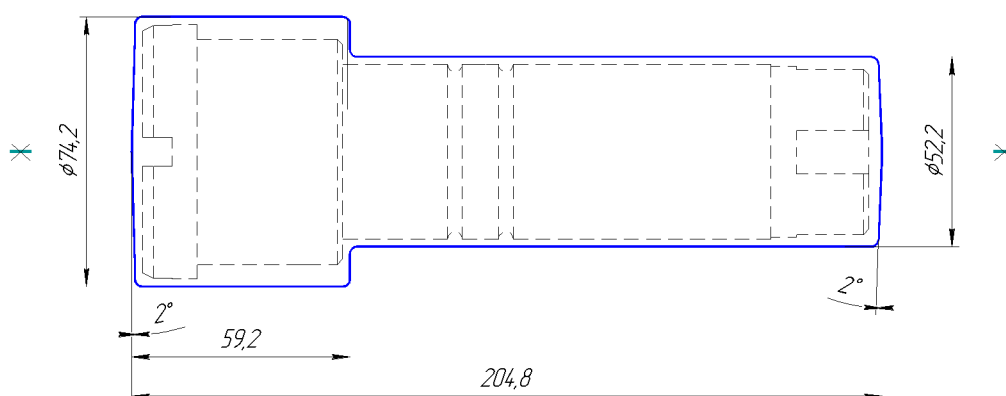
Ескіз заготовки отриманої на КГШП
